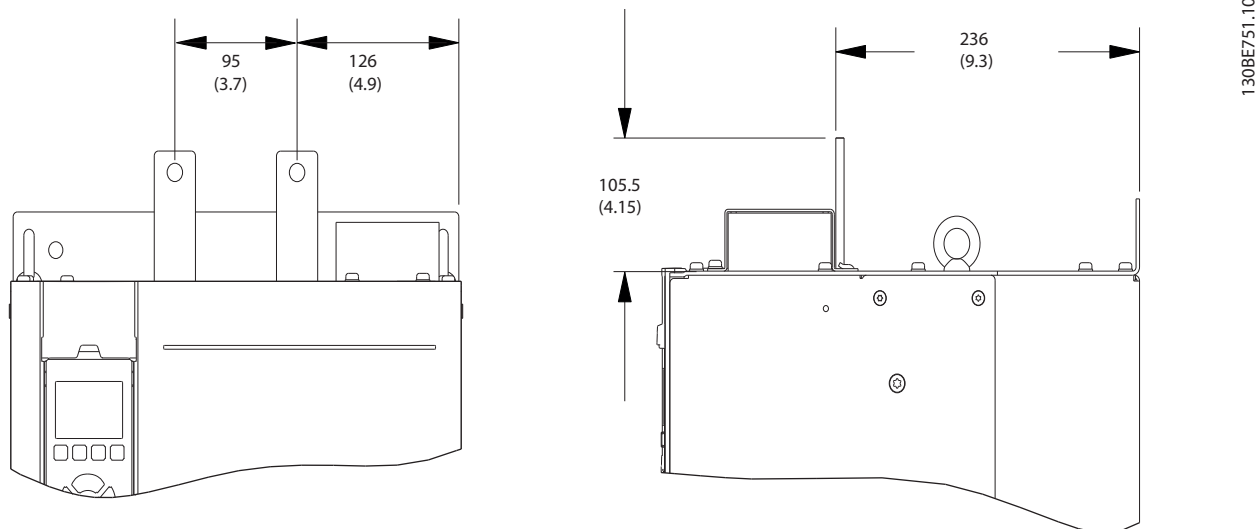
Размеры шины постоянного тока (вид спереди и сбоку)
